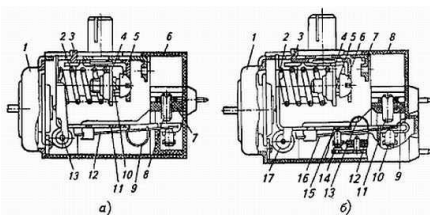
Конструкция терморегуляторов: а — Т-110: 1 — термочувствительная система; 2 — пружина; 3 — ползун; 4 — гайка; 5, 8 — регулировочные винты; 6 — корпус; 7 — колодка; 9 — перебрасывающаяся пружина; 10 — контровочная пружина; 11, 12 — рычаги; 13 — ось; б — Т-144: 1 — термочувствительная система; 2 — пружина; 3 — ползун; 4 — гайка; 5 — контровочная пружина; 6, 11 — регулировоч-
